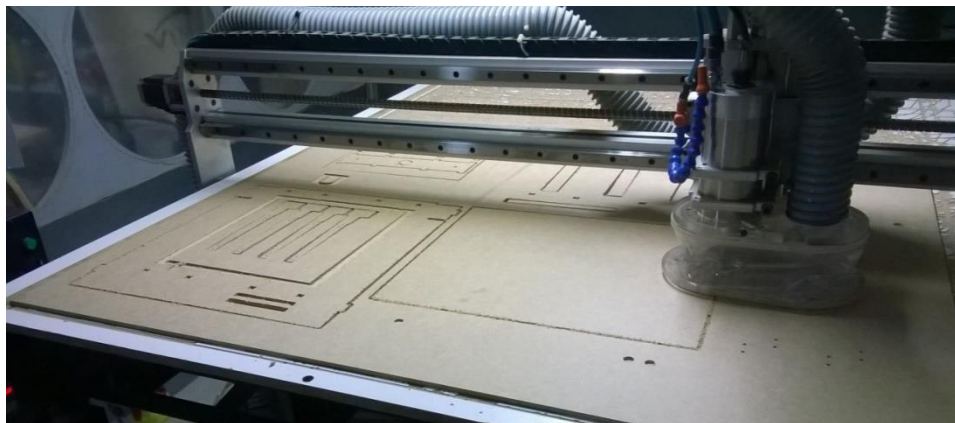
Máquina de corte 2D Router. Momento do corte de protótipo para estrutura de impressora 3D
